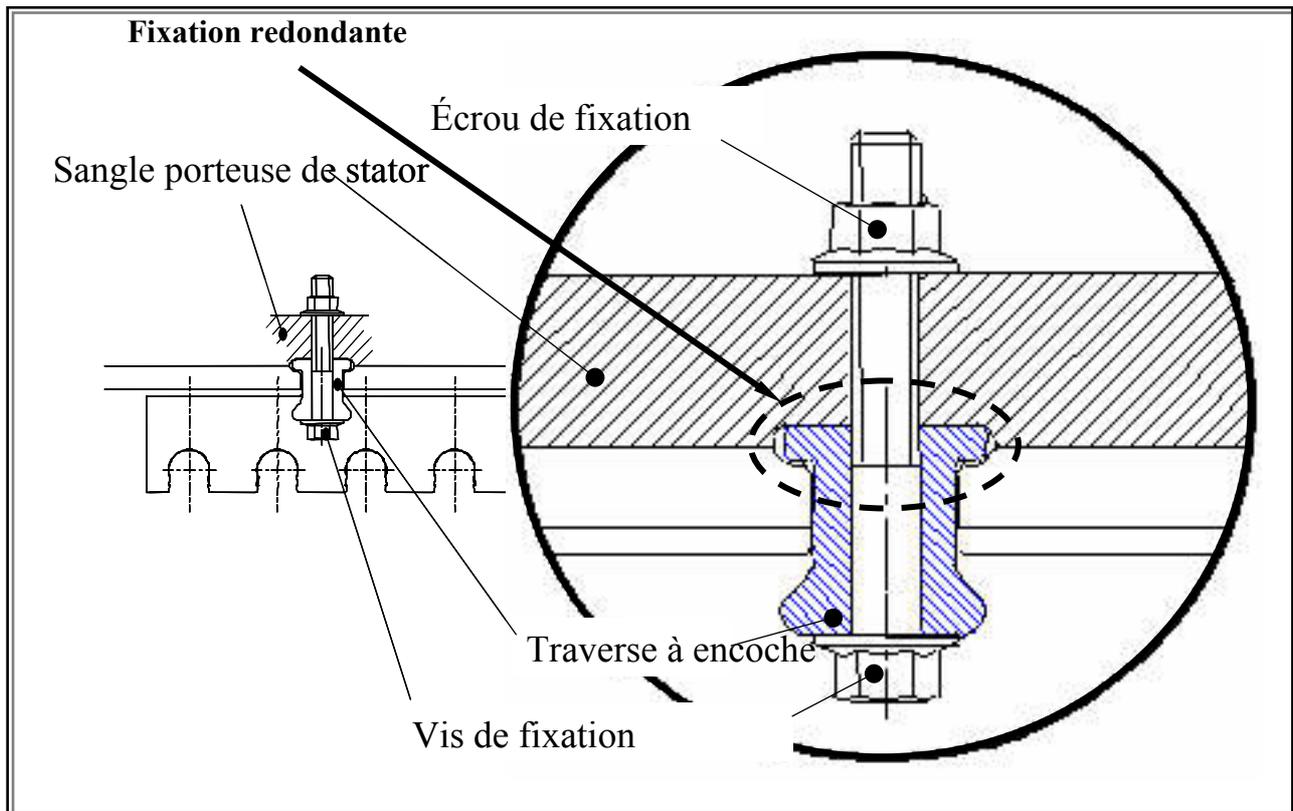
Exemple de différentes fixations redondantes d'un paquet de tôles statoriques sur un bras en porte-à-faux en acier
